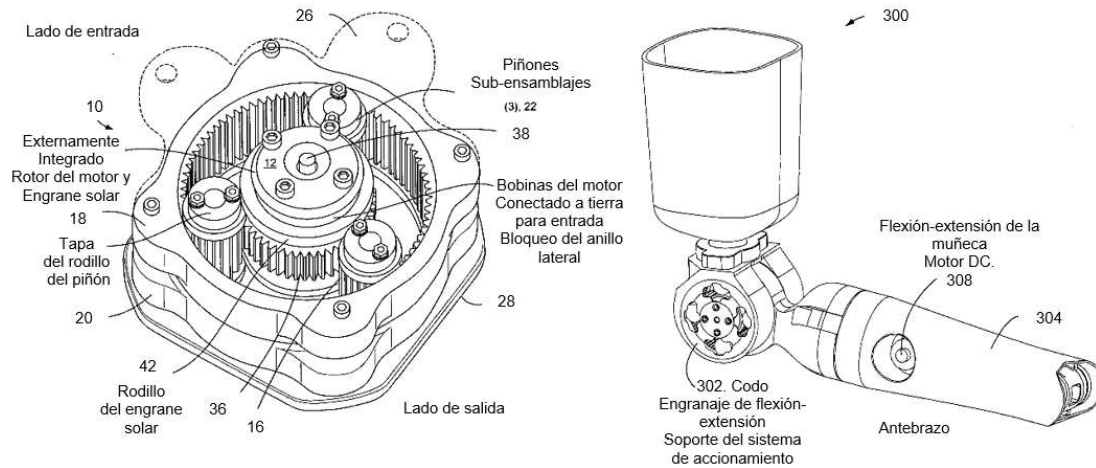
Gear bearing drive (Weinberg, Mavroidis, y Vranish, 2011)
